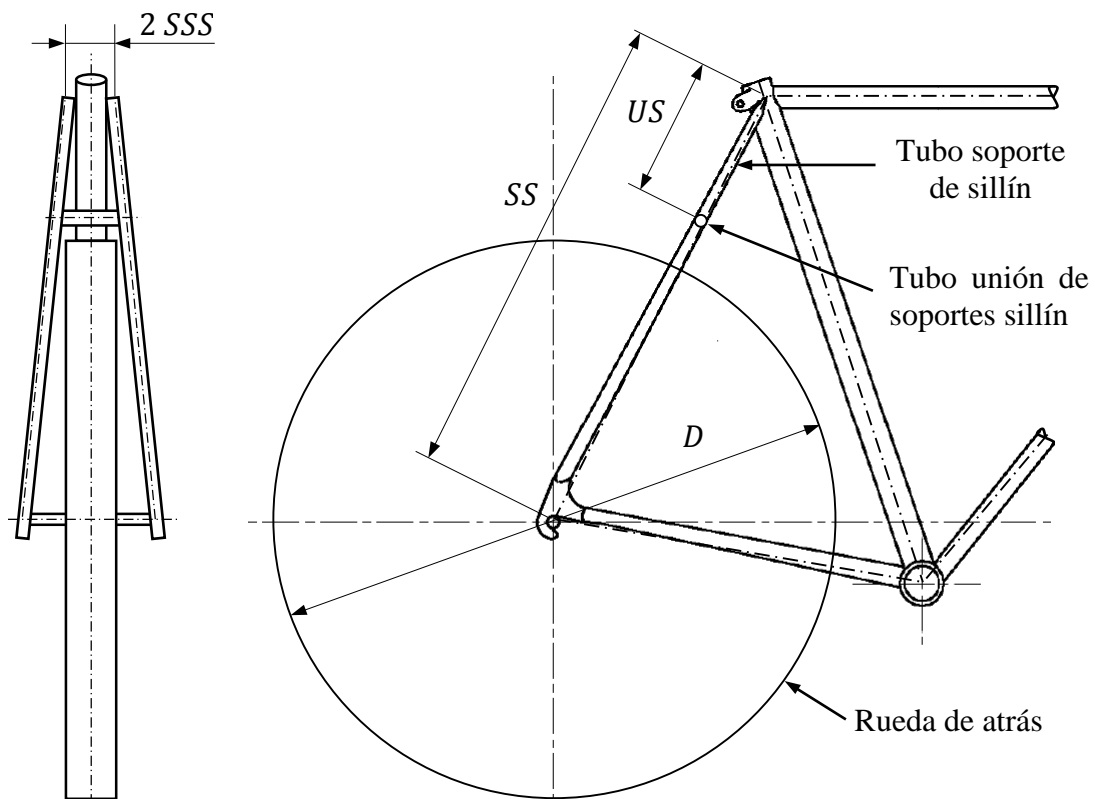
Configuración geométrica de los tubos soportes de sillín.
